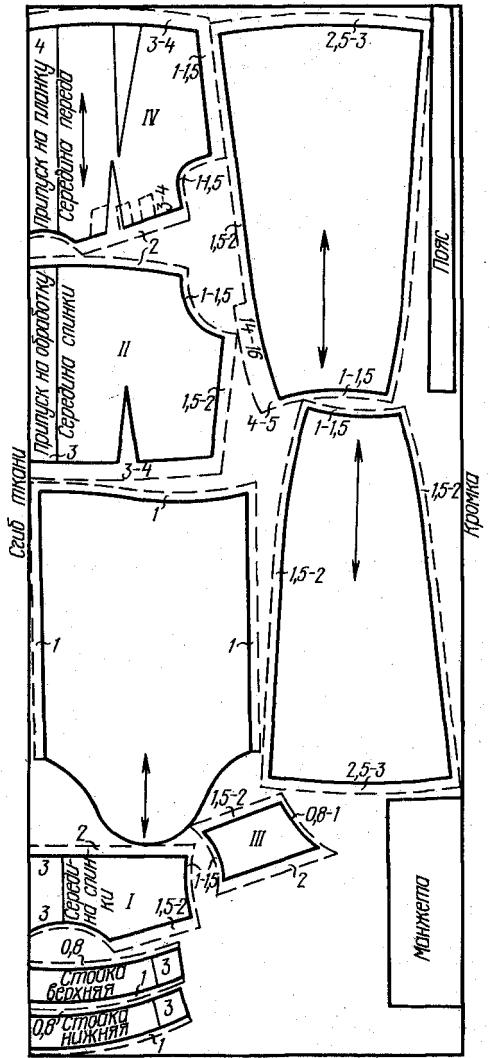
Раскладка выкроек на ткани и раскрой платья на кокетке
